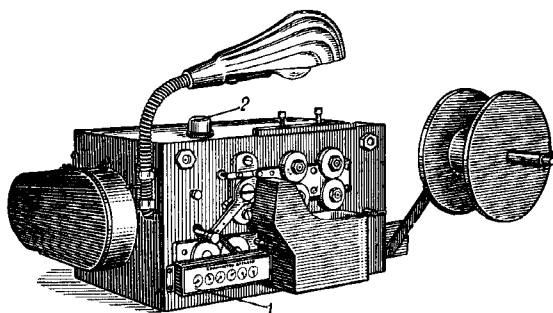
Пружинонавивочный автомат для изготовления пружин малых размеров.
